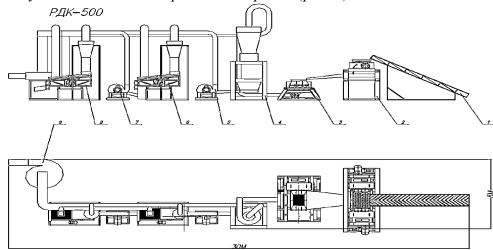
Схема линии по переработке шин РДК-500. 1— транспортёр; 2— верхний шредер; 3— нижний шредер; 4— дефибратор металлического корда; 5—первая роторная дробилка; 6— первое вибросито; 7— вторая роторная дробилка; 8— второе вибросито; 9— вентилятор высокого давления.
